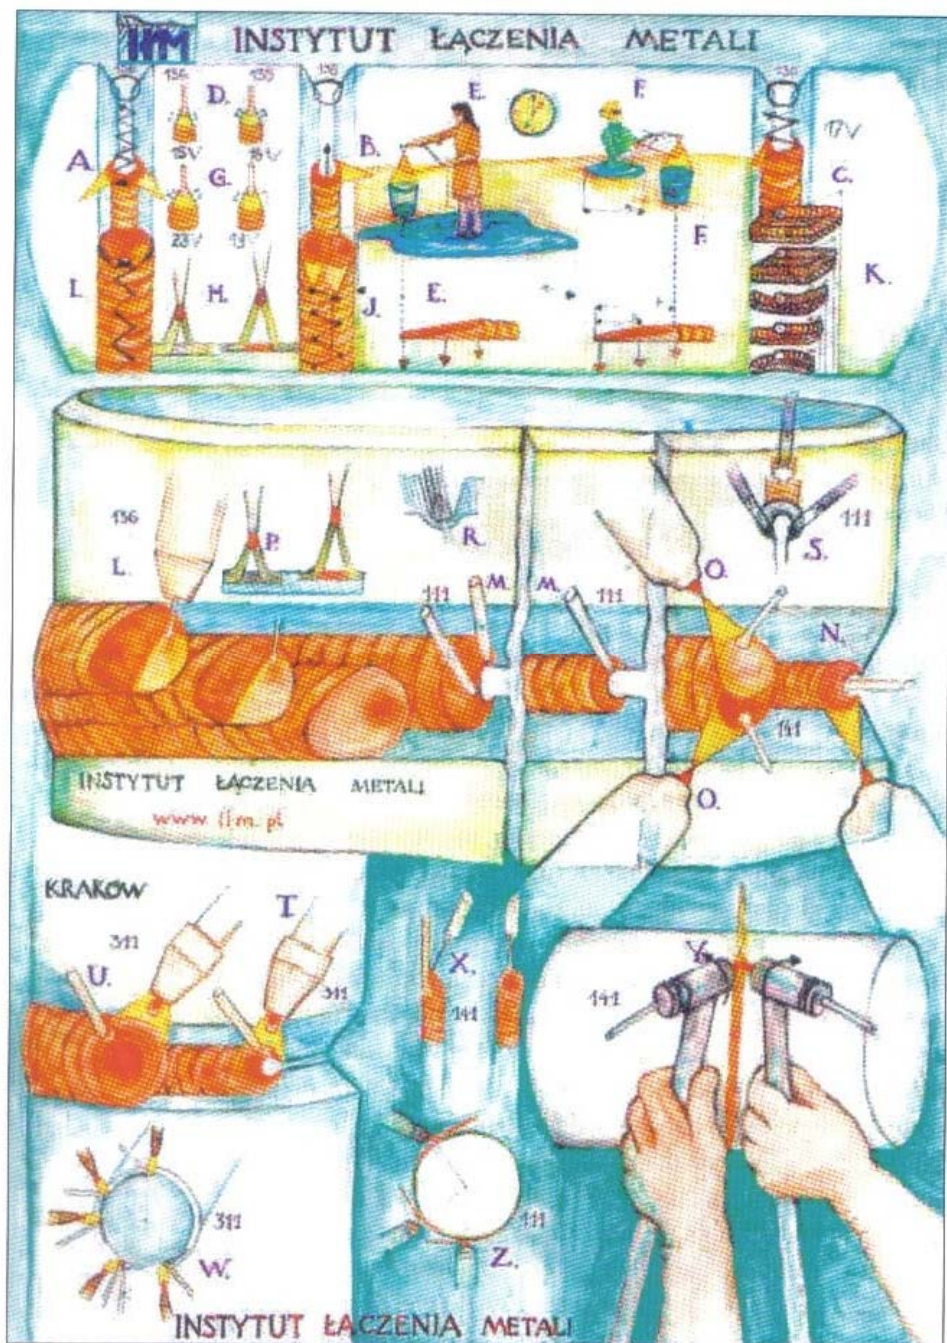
Графическое изображение влияния физики процесса на технику сварки труб из аустенитной стали (картина Катажины Туз «Алфавит сварки труб из аустенитной стали», www.ilm.pl/polska/kal.htm): А, В, С, J, K, L — траектория MAG-сварки сплошной и порошковой проволокой; М, R, S — выполнение провара электродом с основным покрытием при меняющейся ширине зазора; N, O — выполнение провара и второго прохода методом TIG; U, T, W — техника газовой сварки; X, Y, Z — техника TIG-сварки тонкостенных труб в пищевой промышленности; D, G, H — влияние угла раскрытия и длины электрической дуги на глубину провара и температуру ванны; K — влияние траектории движений на толщину выполняемого заполняющего слоя; E, F — влияние размера ванны и положения дуги по отношению к ванне на технику выполнения провара сплошной проволокой при широком (С) и узком (В) зазоре и порошковой проволокой при узком зазоре (А)
